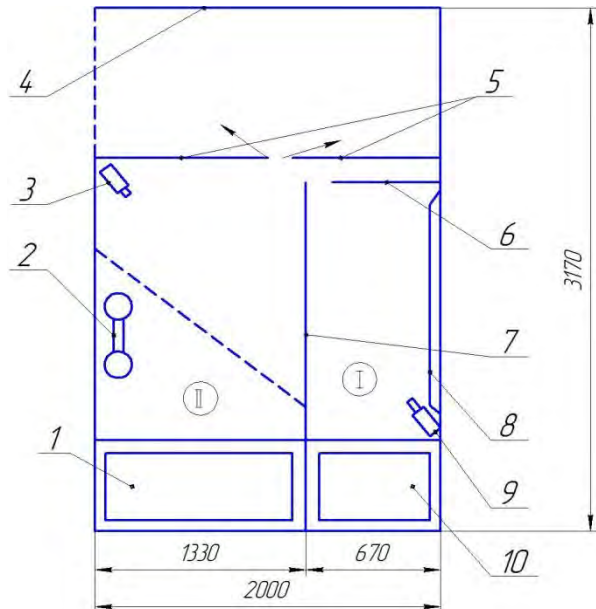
Загальний вид та схема станка ОСМ-120:
